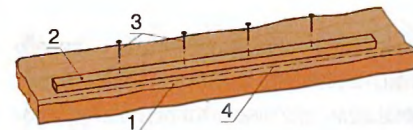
Простейшее приспособление — упорная планка: 1 — необрезная доска; 2 — упорная планка; 3 — гвозди; 4 — линия реза.
